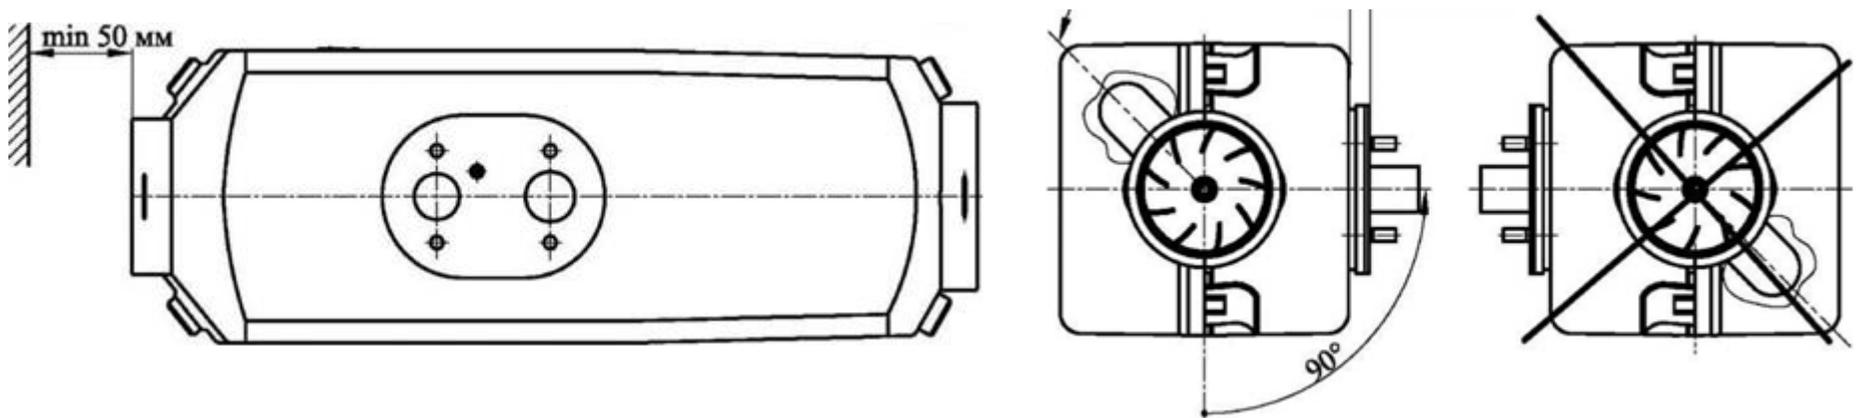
Размеры монтажных отверстий для установки нагревателя
